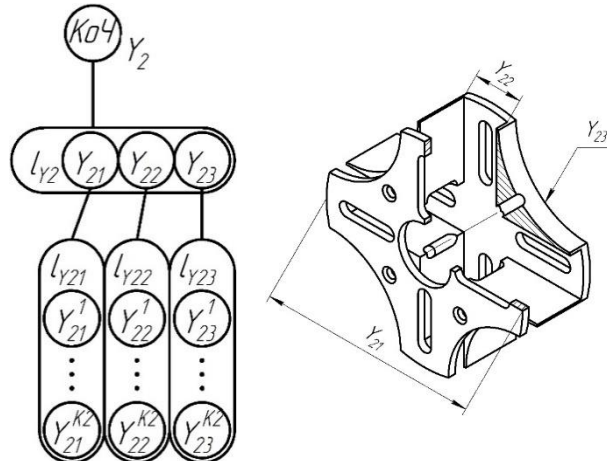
Ребро описывающее корпусную часть сборного шлифовального инструмента
